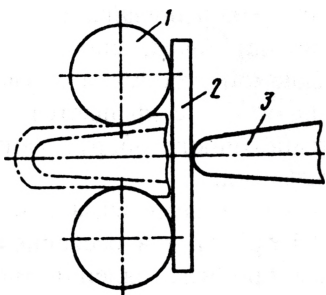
Схема прокатки параболических заготовок малолистовых рессор на профильной оправке
